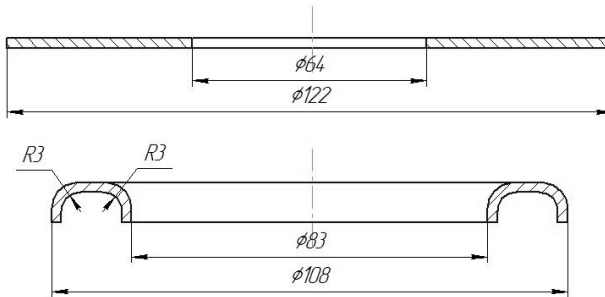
Геометрические размеры заготовки и кольцевого образца
